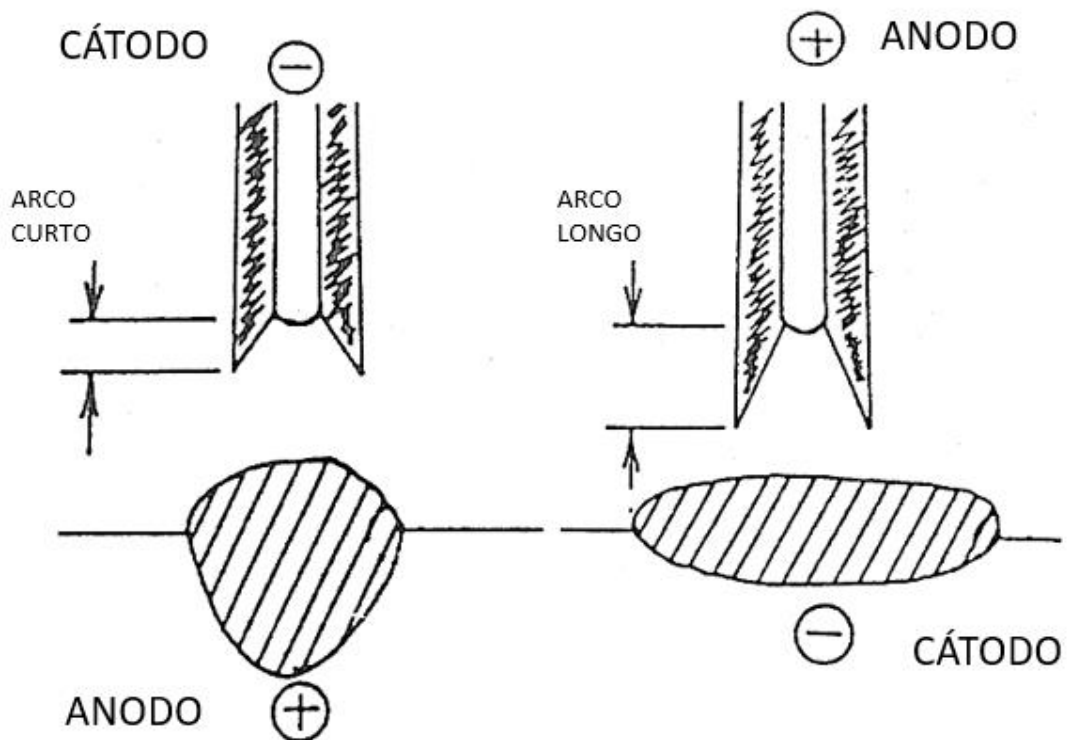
Efeito da polaridade na forma do cordão de solda em soldagem subaquática molhada..
